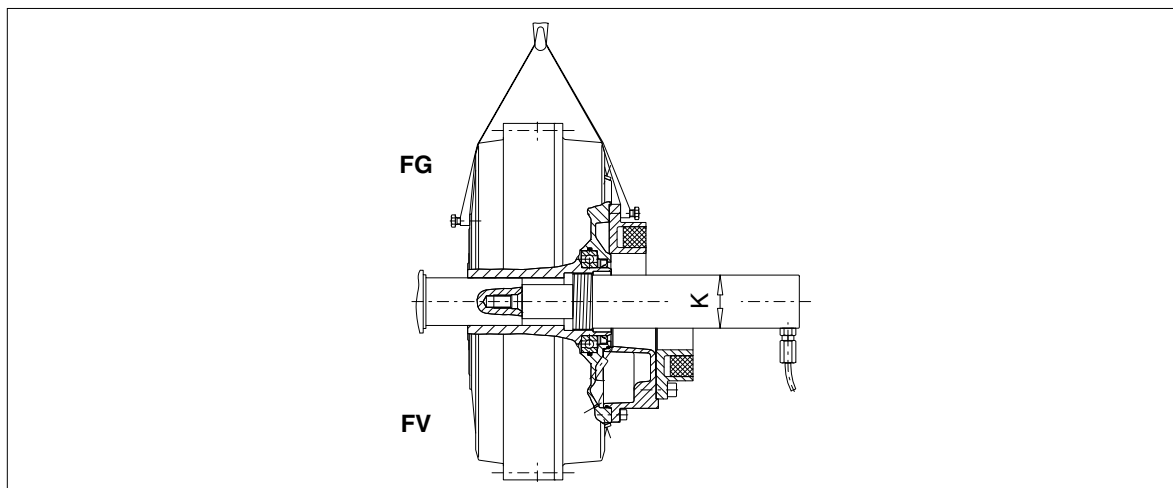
Ausbau der FLUDEX-Kupplung mit hydraulischer Spindel oder Hydraulikzylinder
